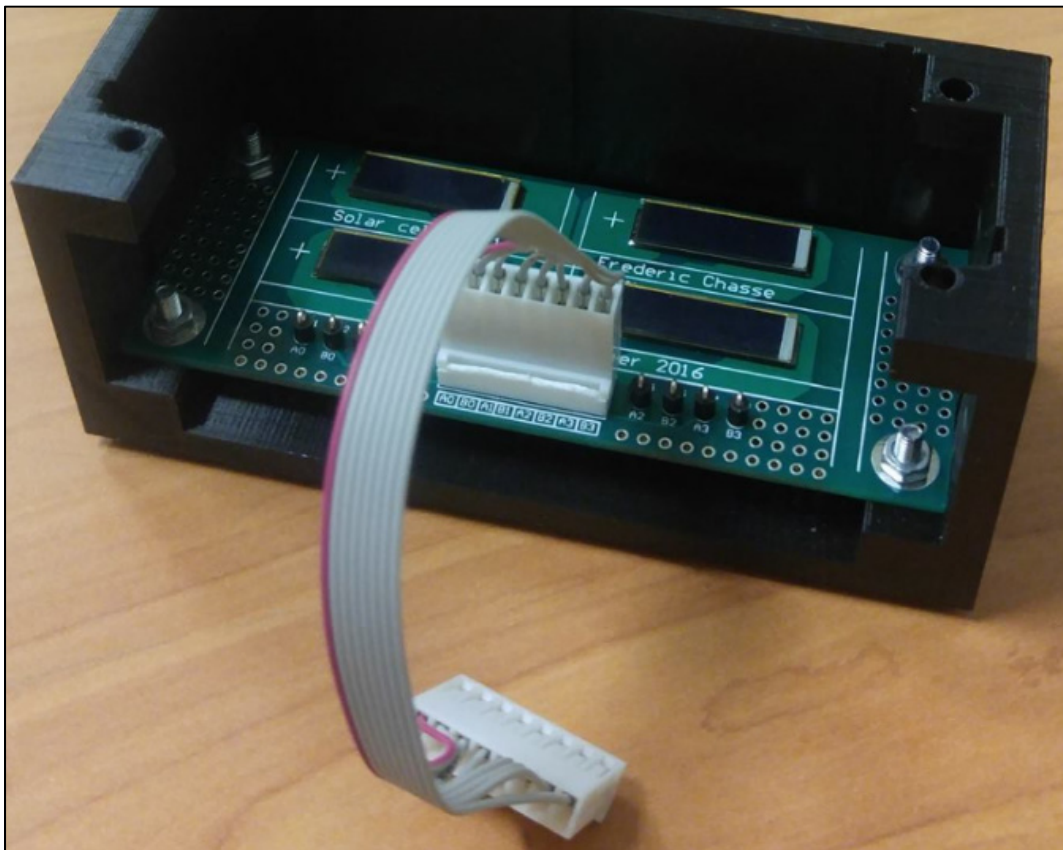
Photo du PCB assemblé et monté dans son boîtier
